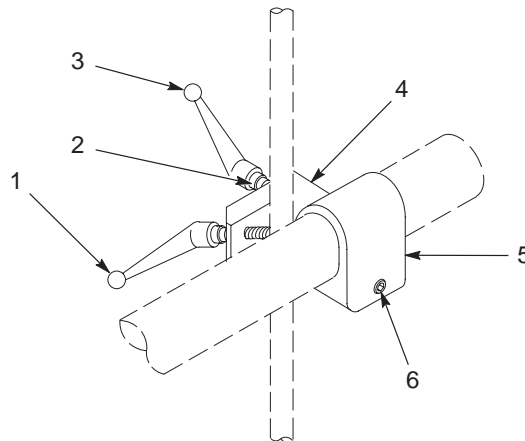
Standaard pistoolstanggroep voor buisbevestigd pistool
